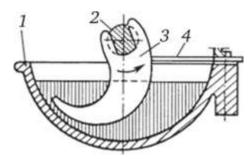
Режущий механизм куттера: 1 – чаша; 2 – вал; 3 – нож; 4 – гребенка
